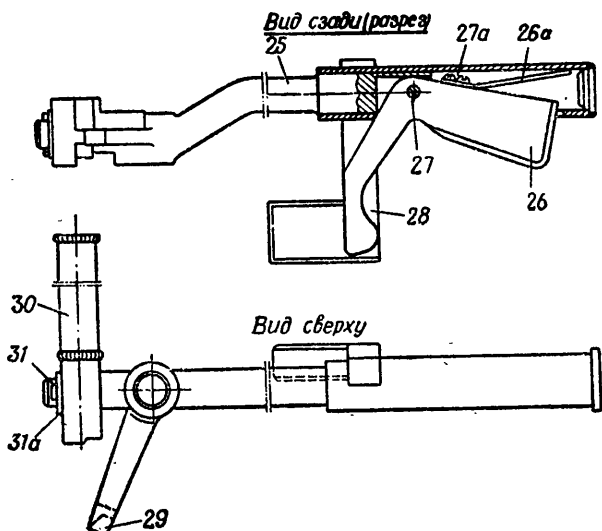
Рукоятка ствола (С601-10) старой конструкции:
